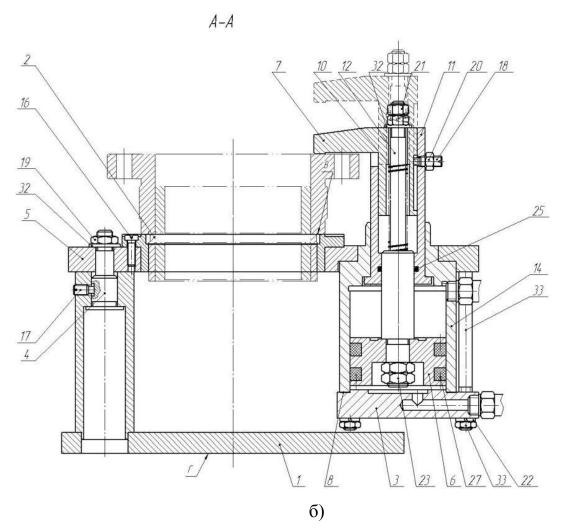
Приспособление для обработки отверстий в стакане
